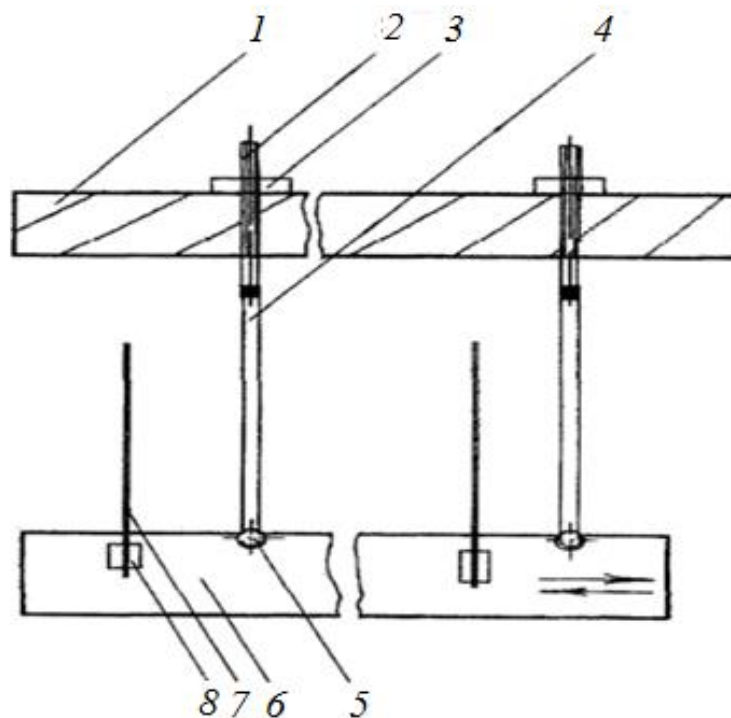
Схема универсальной подвески: 1 – рама, 2 – шпилька, 3 – гайка, 4 – плоская пружина, 5 – шарнир, 6 – решетный стан, 7 – металлический стержень, 8 – резьбовое крепление
